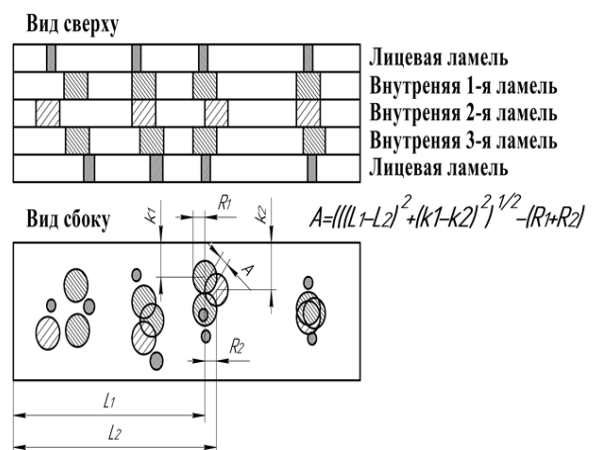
Расчетная схема определения величины перекрытия сучков А
